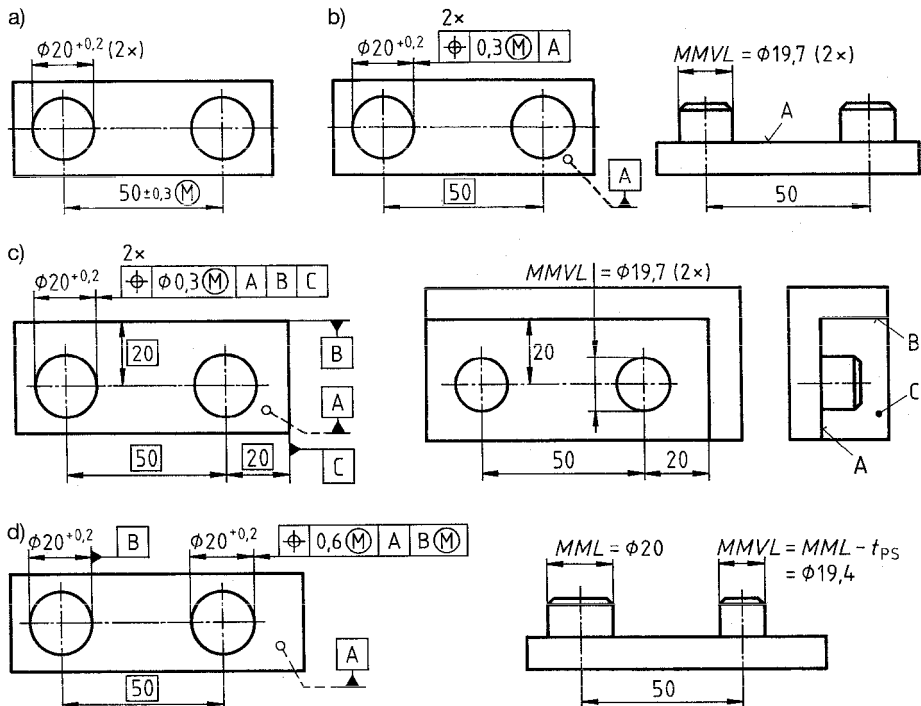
Prüfung von Lochbildern mit starren Lehren. a) schwimmendes Lochbild, nicht normgerecht toleriert (wie Bild 4.22 a), b) korrekte Positionstolerierung und Funktionslehre dazu; c) Lochbild mit vollständigem Bezugssystem und Lehre dazu; d) Lochbild ähnlich b, aber mit Bezugsbohrung, mit zugehöriger Lehre
